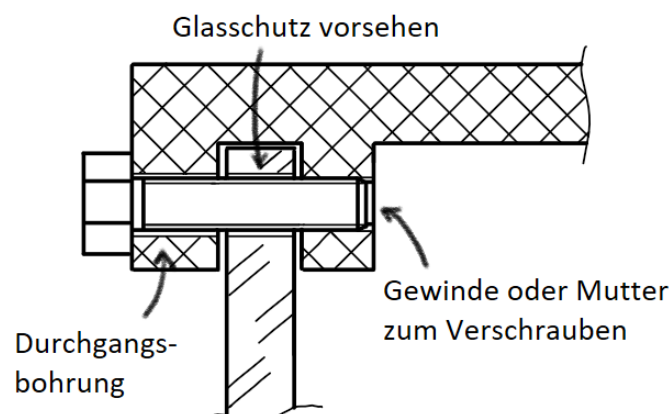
Verschraubung des Deckels am Borosilikatglaszylinder mittels Sechskantschraube
